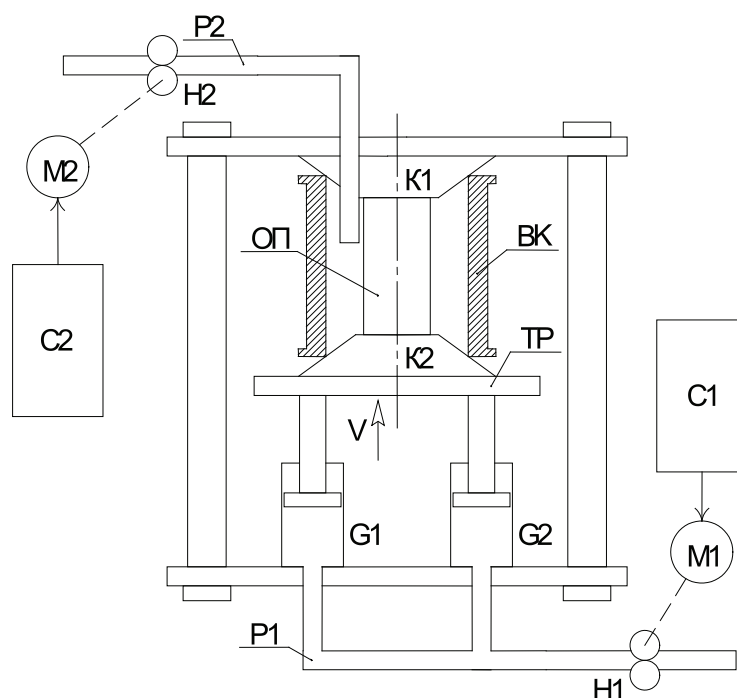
Установка гидрорастяжения кольцевых заготовок:
